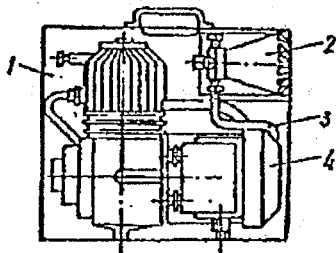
Фарбувальний агрегат СО-74А: 1 - контейнер; 2 - фарборозпилювач СО-19А; 3 - рукав 4 - компресор СО-45
